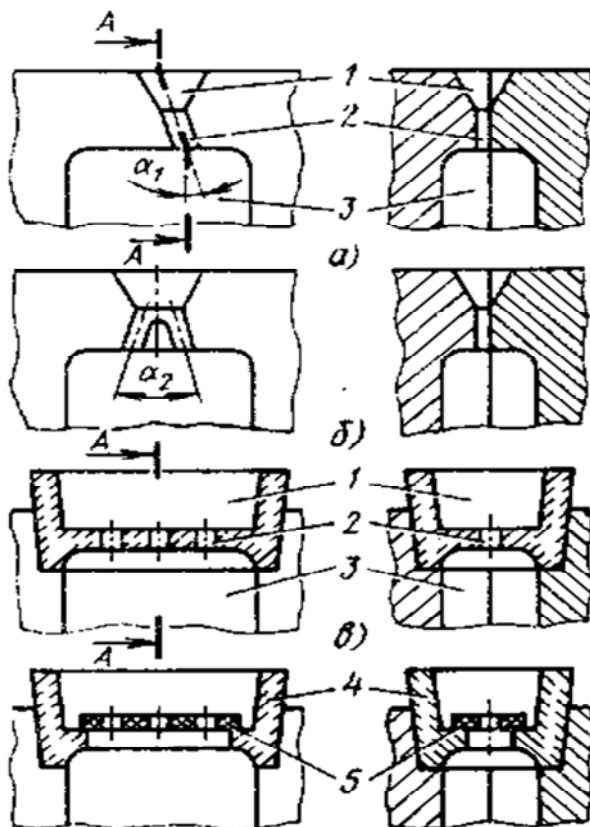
Схемы литниковых систем для заливки сверху кокилей с вертикальным разъемом
